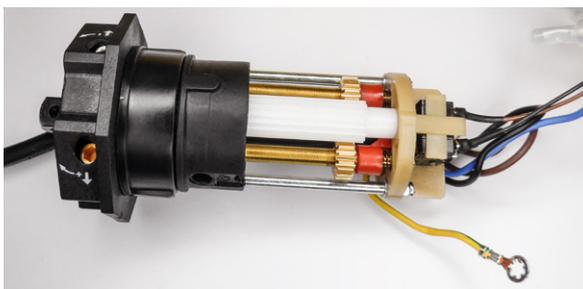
Die Mechanik für die Ansteuerung der Endlagenschalter eines mechanischen Rohrmotors
